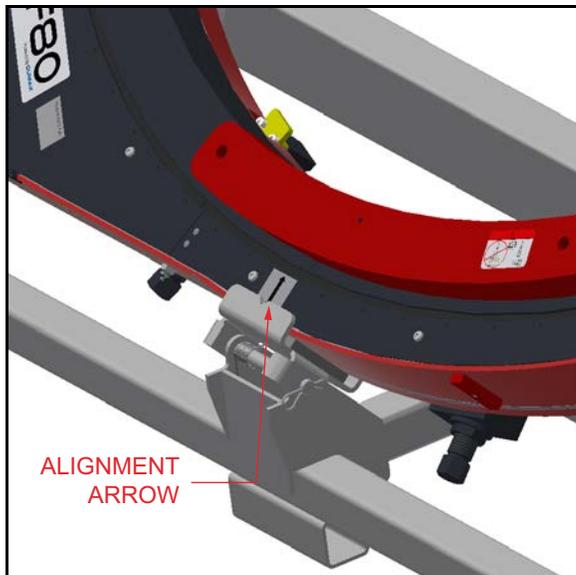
FLÈCHE D'ALIGNEMENT (ILLUSTRATION AVEC LA MACHINE ODF80)
